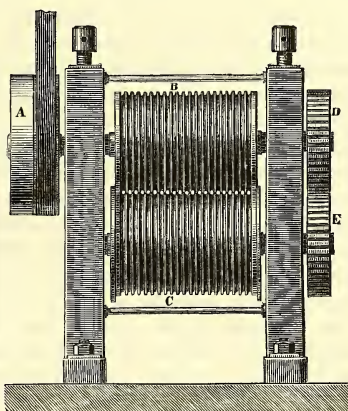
Appareil Hancock pour la préparation des fils de gutta-percha.
